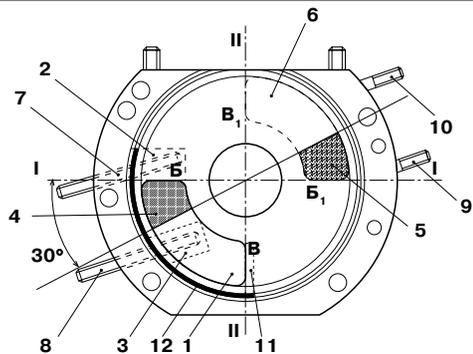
Схема расположения нового впускного отверстия верхнего цилиндра.
